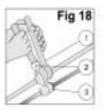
1. Chiave fissa 2. Chiave 3. Collegamento
